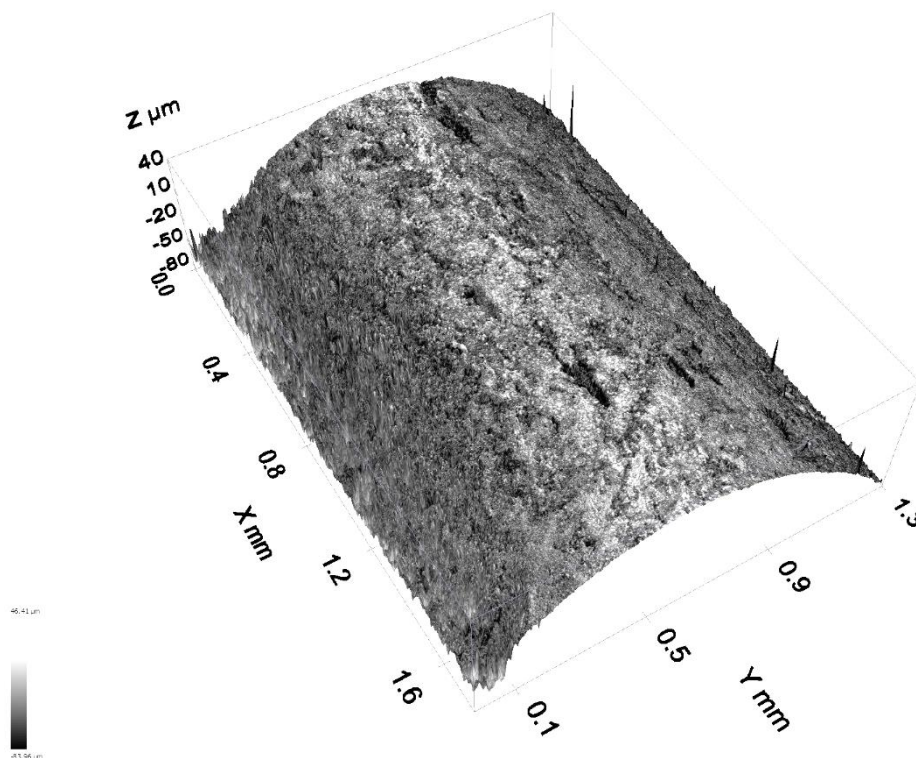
Imagem tridimensional da superfície do corpo do parafuso.
